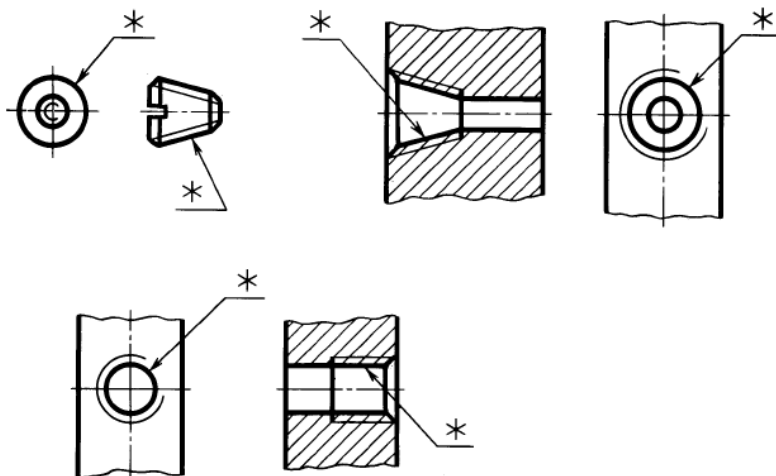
Способы нанесения обозначения конических и трубной цилиндрической резьбы
